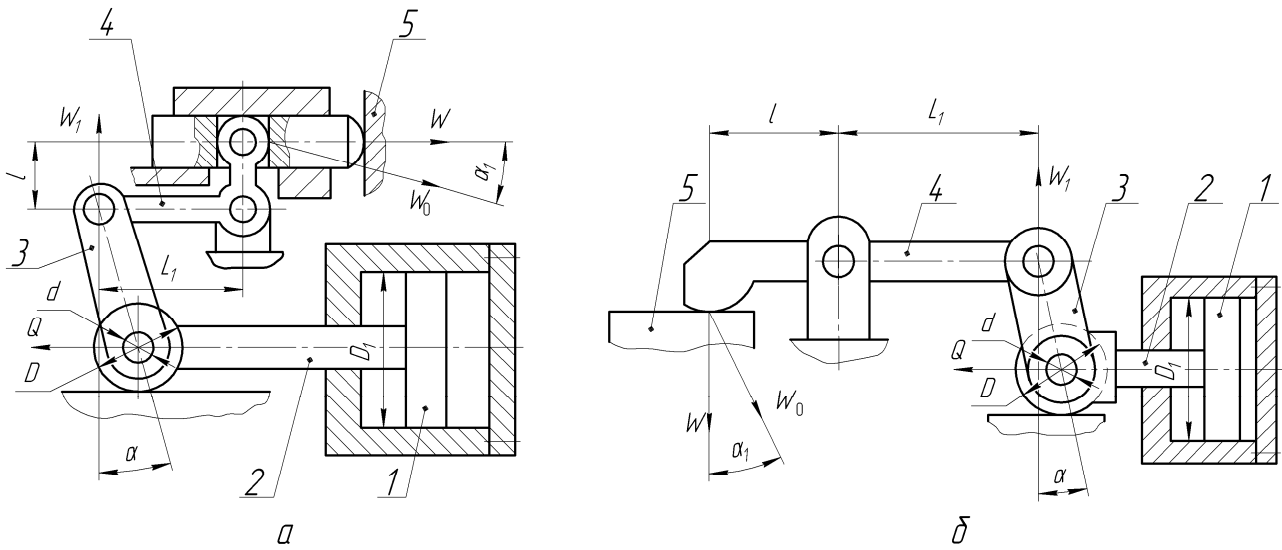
Будова й параметри різних типів пневматичних затискачів: *а* – з важільним механізмом-підсилювачем (1 – поршень; 2 – шток; 3 – тяга; 4 – важіль; 5 – вісь; 6 – прихоплювач; 7 – деталь); *б* – з важільним механізмом (1 – поршень; 2 – шток; 3 – тяга; 4 – важіль; 5 – деталь); W – зусилля затискання деталі; W_0 – зусилля затискача; W_1 – зусилля на важелі; Q – зусилля на штоку; l , l_1 – довжини плечей прихоплювачів і важелів; D_1 – діаметр поршня; α , α_1 – кути напрямку прикладання сил до тяг і деталей
